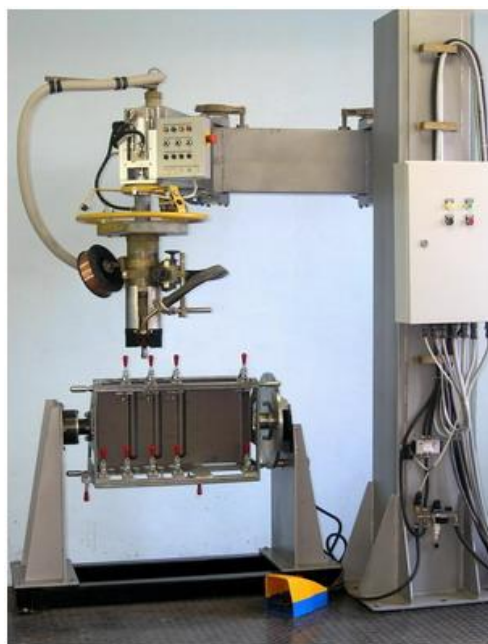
Установка АС307 (НАВКО-ТЕХ)
